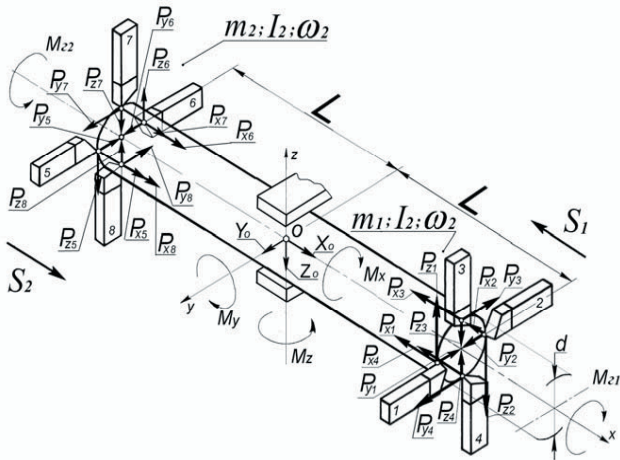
Обработка неподвижной заготовки восемью режущими элементами
